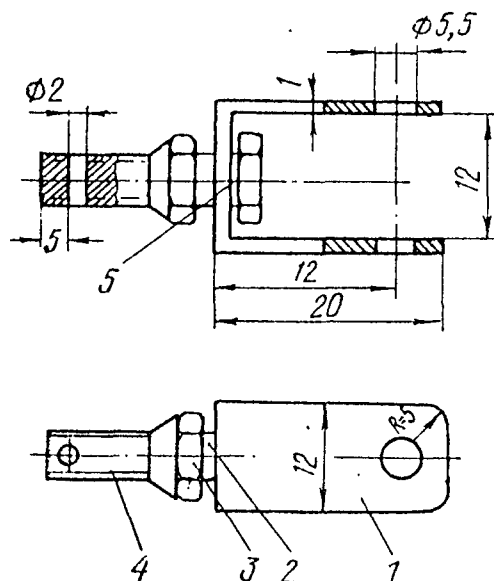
Узел крепления пружины подлокотников кресел пилотов:
